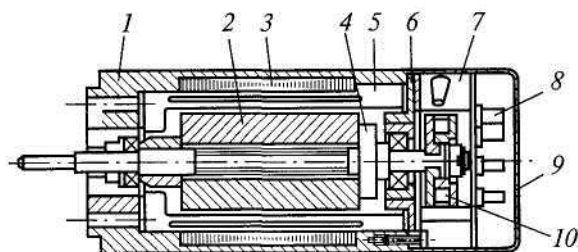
Бесконтактный исполнительный двигатель типа ДБУ:
